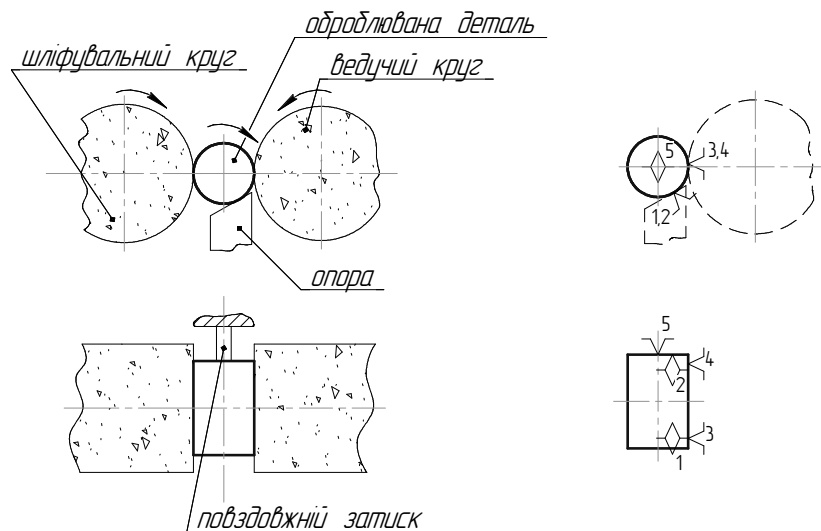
Схема базування вала по оброблюваній поверхні при безцентровому врізному шліфуванні.
